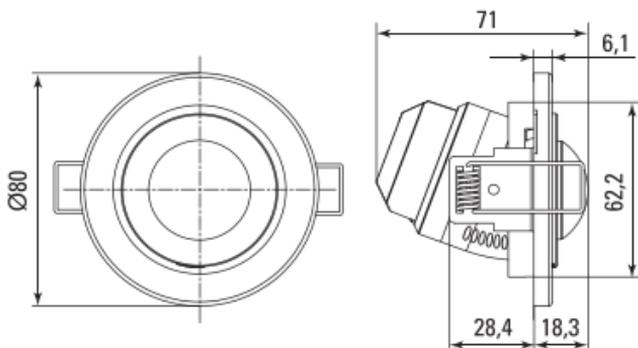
Габаритные и установочные размеры датчика MS-300
